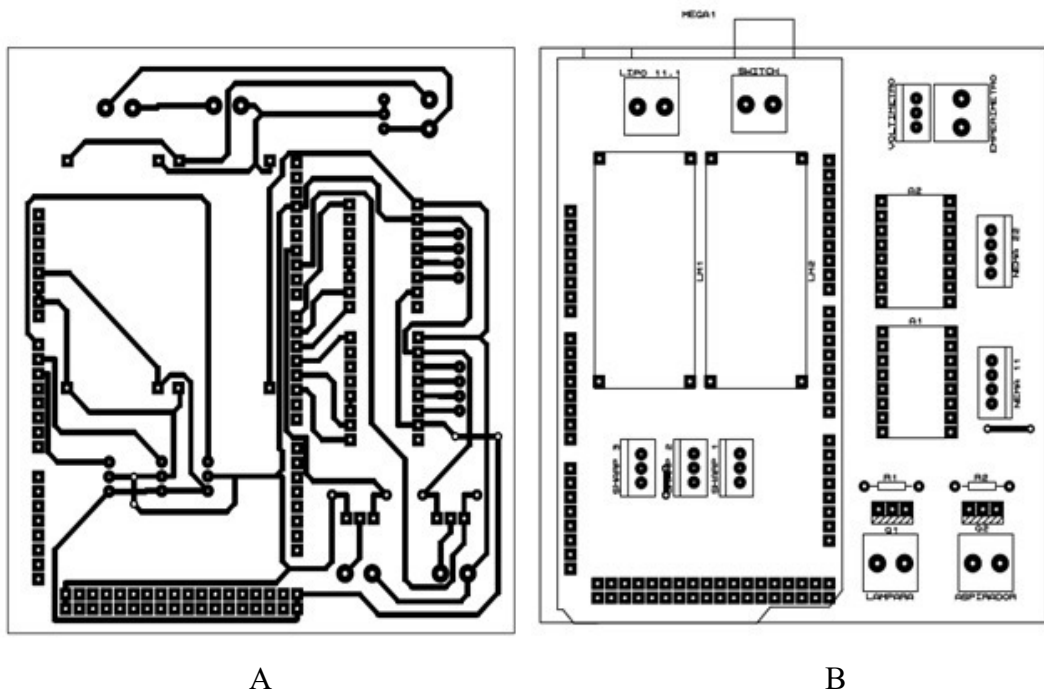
Circuito de la placa PCB, A) Vista inferior, y B) Vista superior
